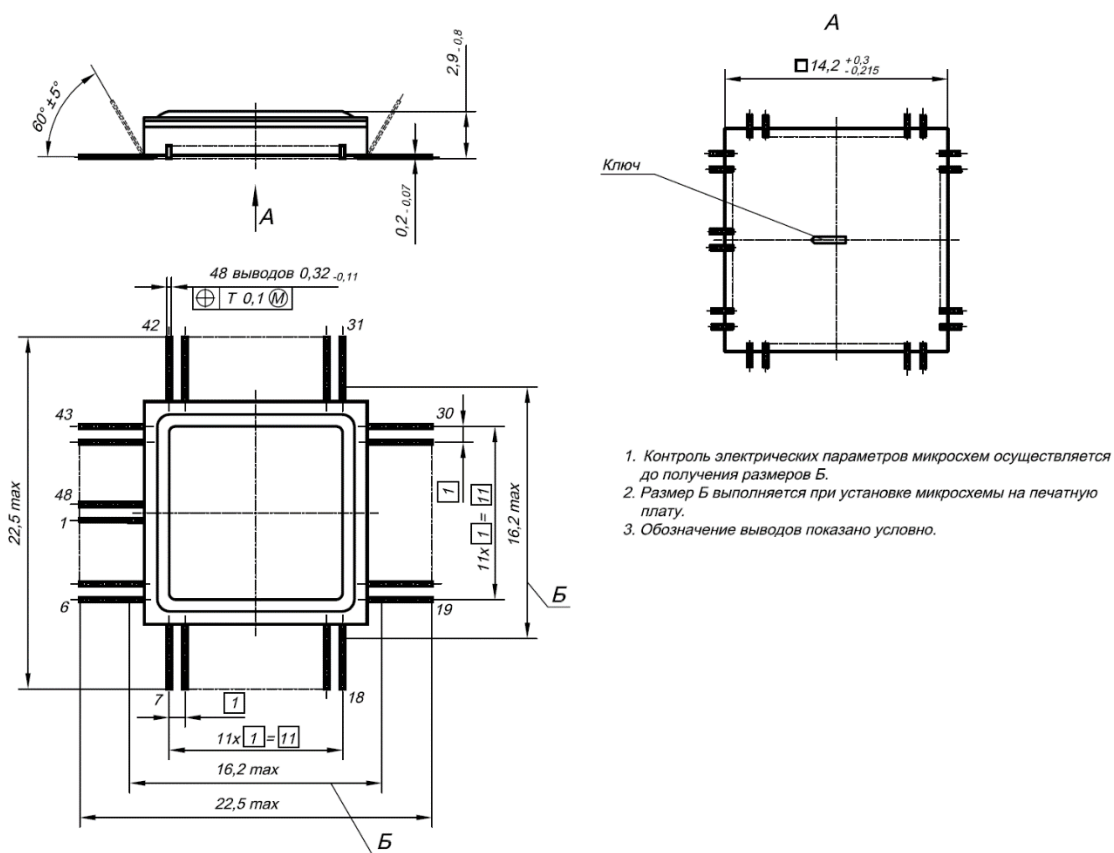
габаритный чертеж микросхемы N1582ВЖЗБ-0305 в корпусе N16.48-2В
